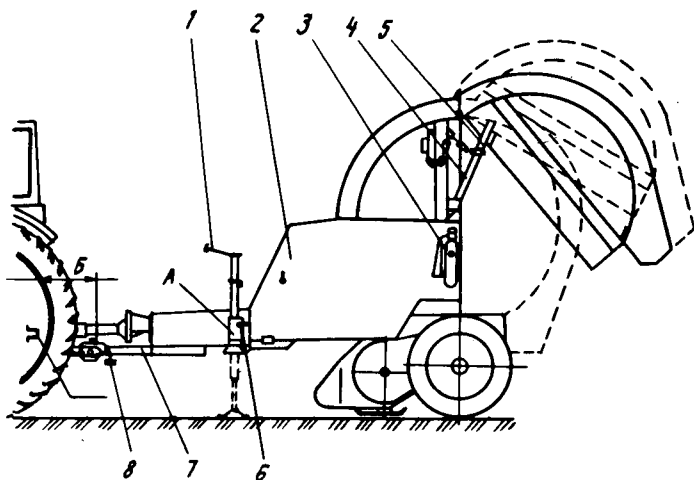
Подготовка пресс-подборщика ПР-Ф-750 к работе: 1 - опора; 2 - кожух левый; 3 - огнетушитель; 4 - гидроцилиндры открывания прессовальной камеры; 5 - фиксатор; 6 - штырь; 7 - сница; 8 - трос страховочный
